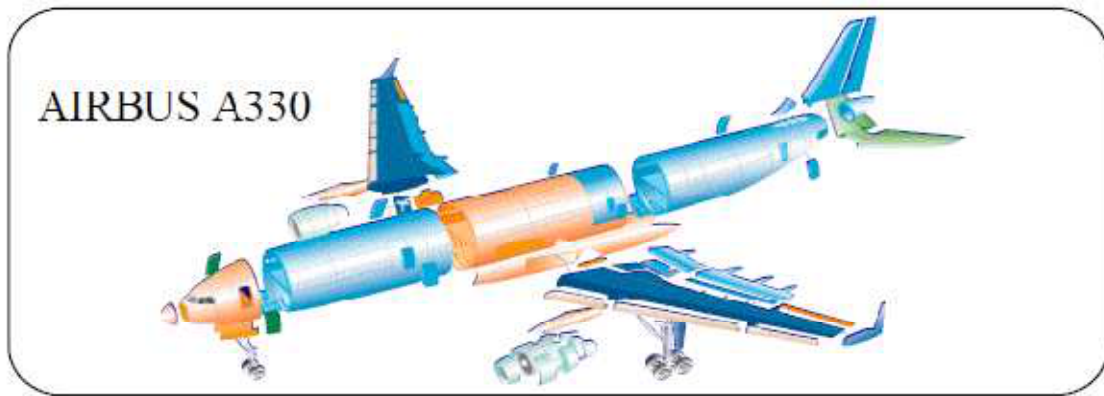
Vue éclatée des différentes portions à assembler d'un A330
